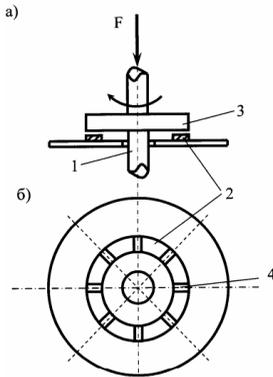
Схема упорного гидродинамического подшипника (вид сбоку и вид сверху)
